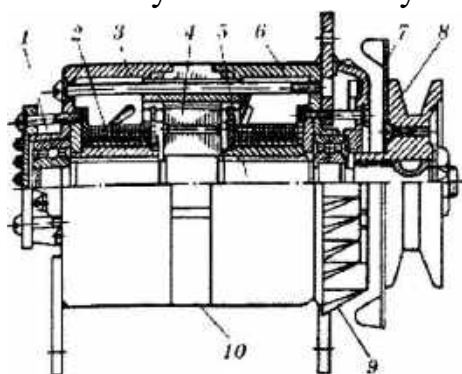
Генератор змінного струму з нерухомими обмотками збудження Г304-Б1: 1 — підшипник; 2 — обмотка збудження; 3 — задня кришка; 4 — ротор; 5 — вал ротора; 6 — передня кришка; 7 — вентилятор; 8 — шків; 9 — корпус випрямляча; 10 — статор.
